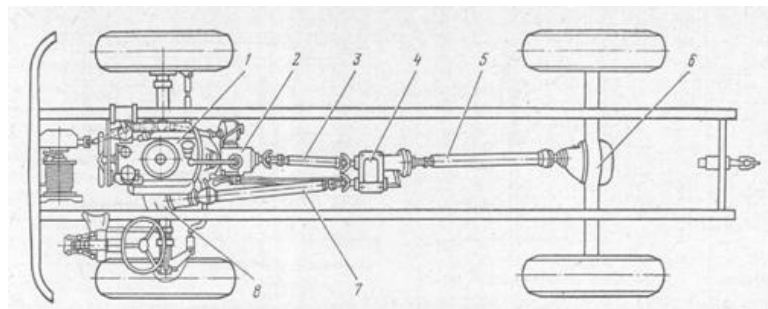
Схема расположения основных агрегатов и механизмов на автомобиле (грузовой автомобиль повышенной проходимости с двумя ведущими мостами ГАЗ-66)
